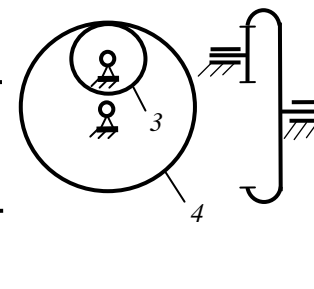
Зубчатая передача с внутренним зацеплением колёс
